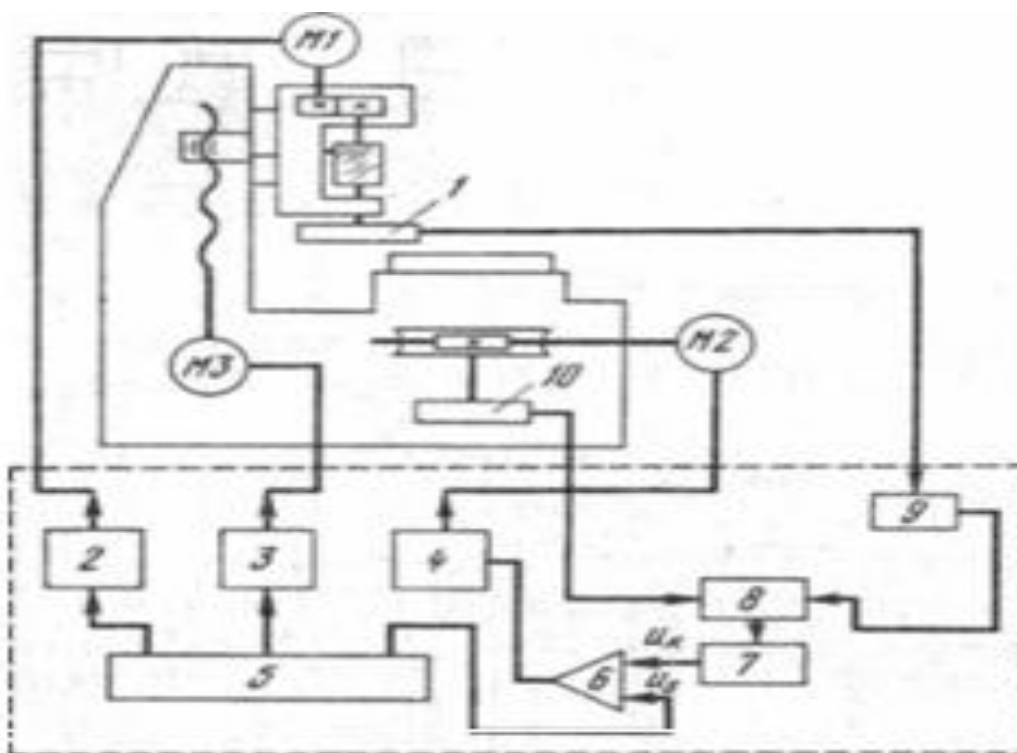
Структурная схема зубофрезерного станка с ЧПУ.
